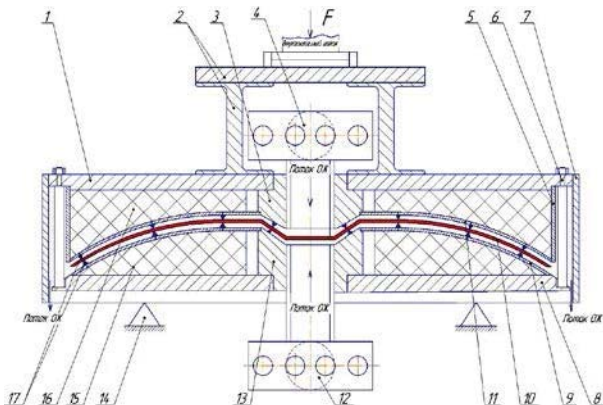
Принципиальная схема устройства закалочного охлаждения дисков: 1 – плита верхняя; 2 – фланец; 3 – вставка верхняя; 4 – коллектор верхний; 5 – кожух внутренний; 6 – упор; 7 – кожух наружный; 8 – плита нижняя; 9 – матрица; 10 – заготовка диска; 11 – пуансон; 12 – коллектор нижний; 13 – вставка нижняя; 14 – опора; 15 – плита монтажная нижняя; 16 – плита монтажная верхняя; 17 – фиксатор
